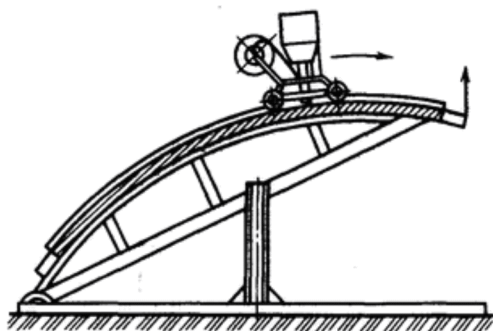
Стенд для автоматической дуговой сварки швов блока
